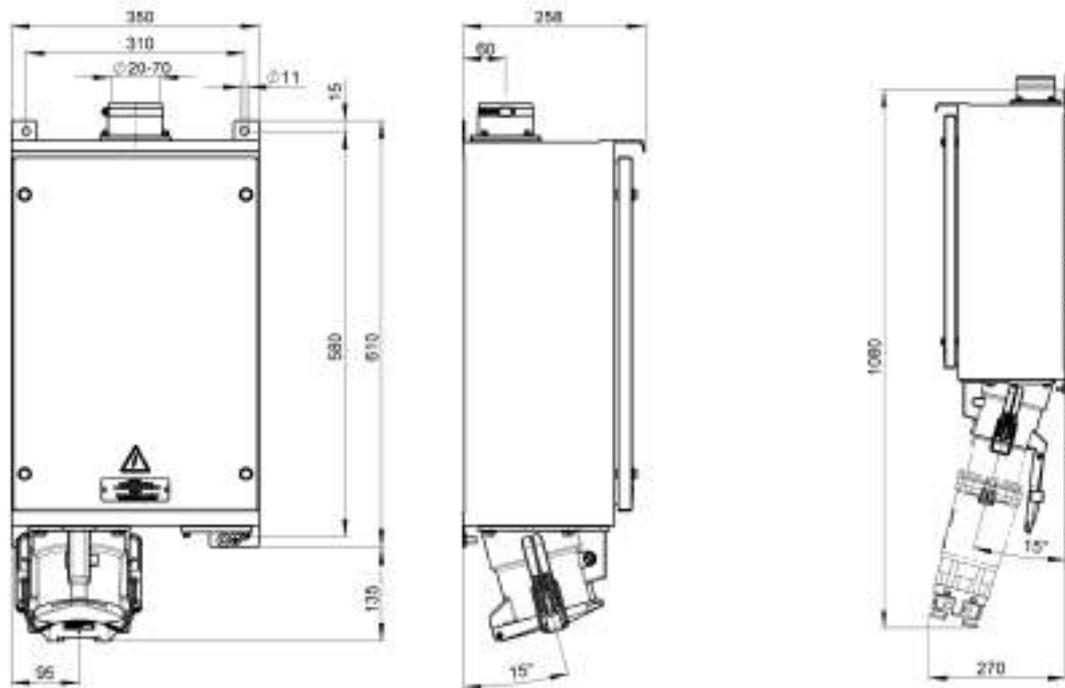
Abmessungen Anschlusskasten mit Blockschütze CUBC D-Line, C-Line (160A – 250 A) in mm
